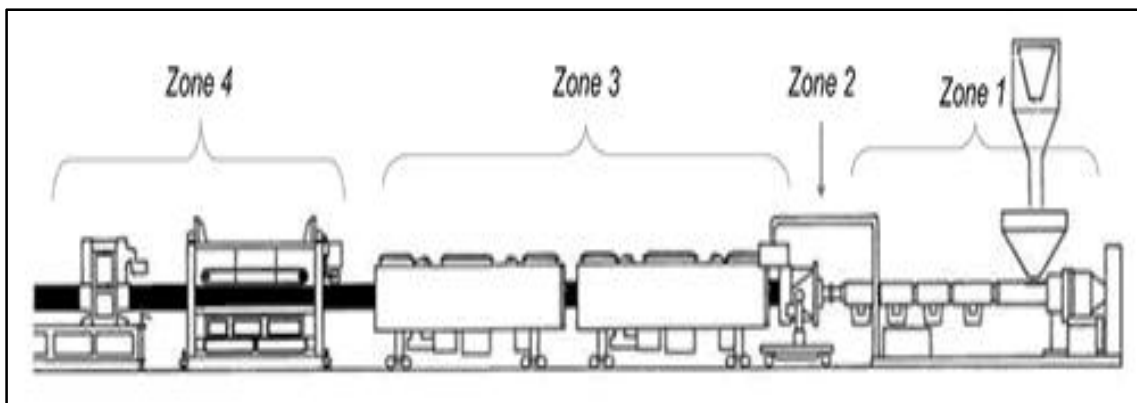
La ligne d'extrusion de tube polyéthylène
